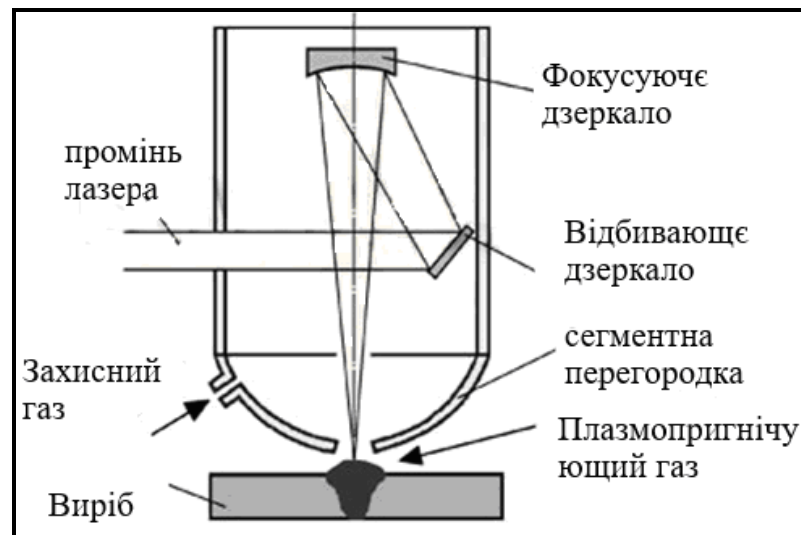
Схема процесу лазерного зварювання [71]
